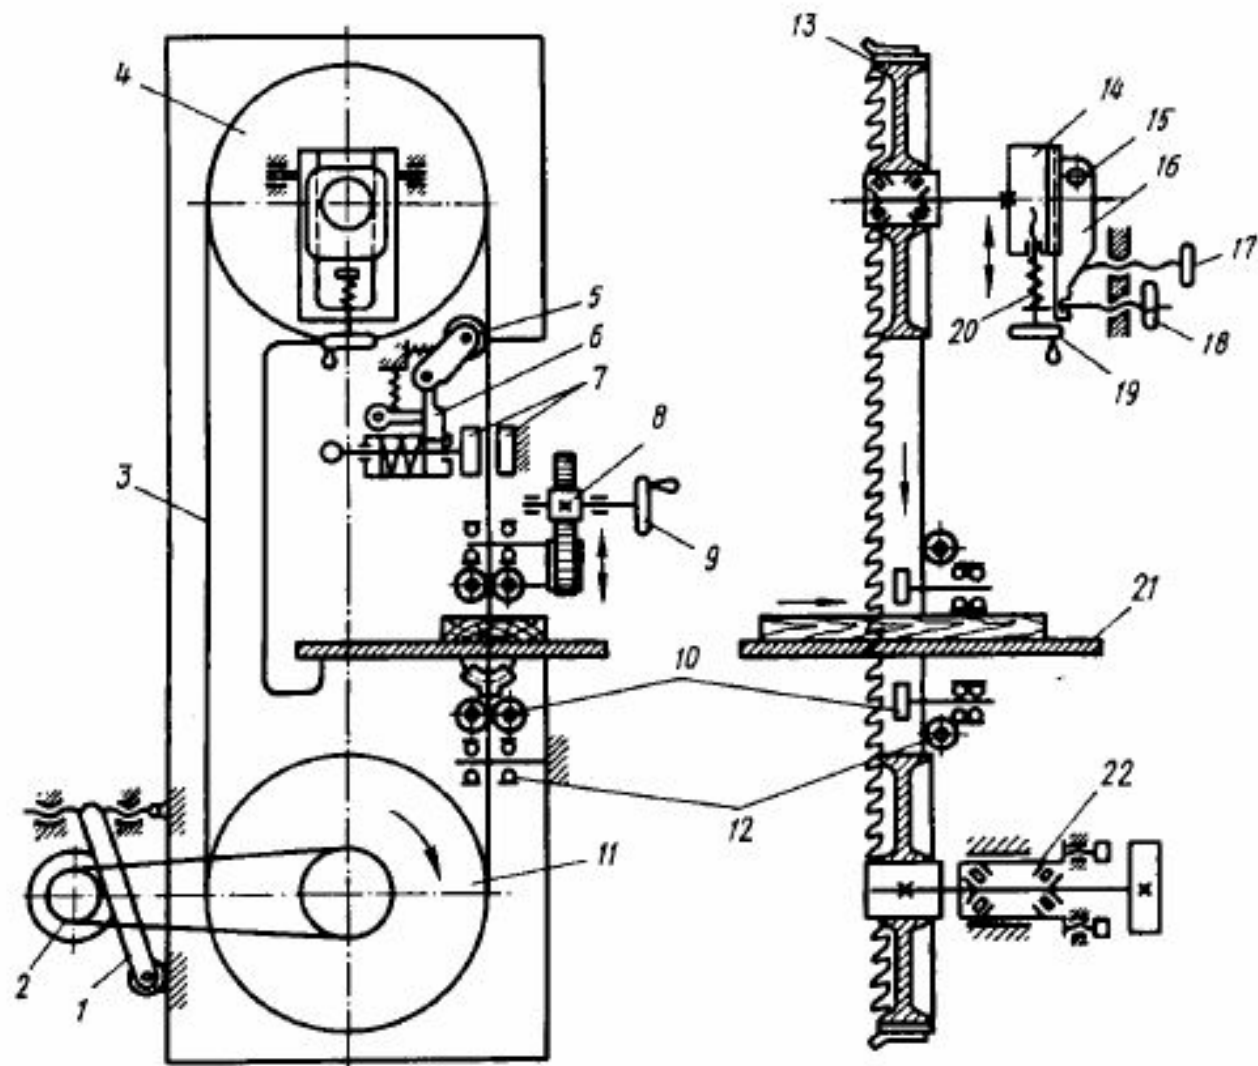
Кинематическая схема столярного ленточнопильного станка ЛС80-6С:
